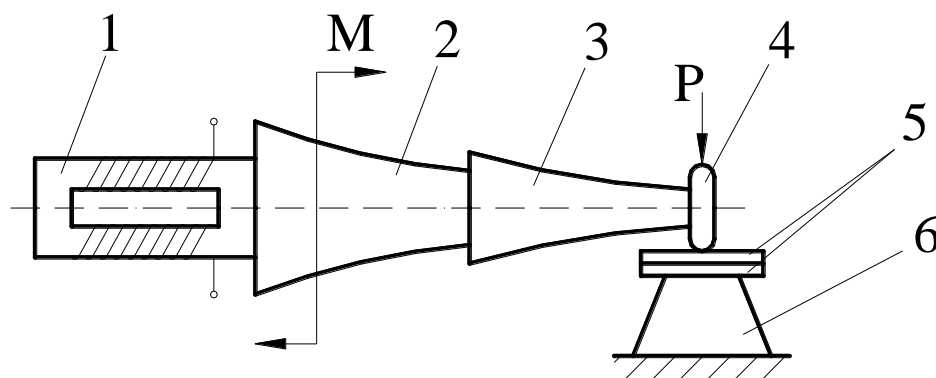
Схема ультразвуковой сварки: 1 — магнитострикционный преобразователь; 2 — трансформатор продольных упругих колебаний; 3 — рабочий инструмент; 4 — наконечник; 5 — свариваемые заготовки; 6 — опора
